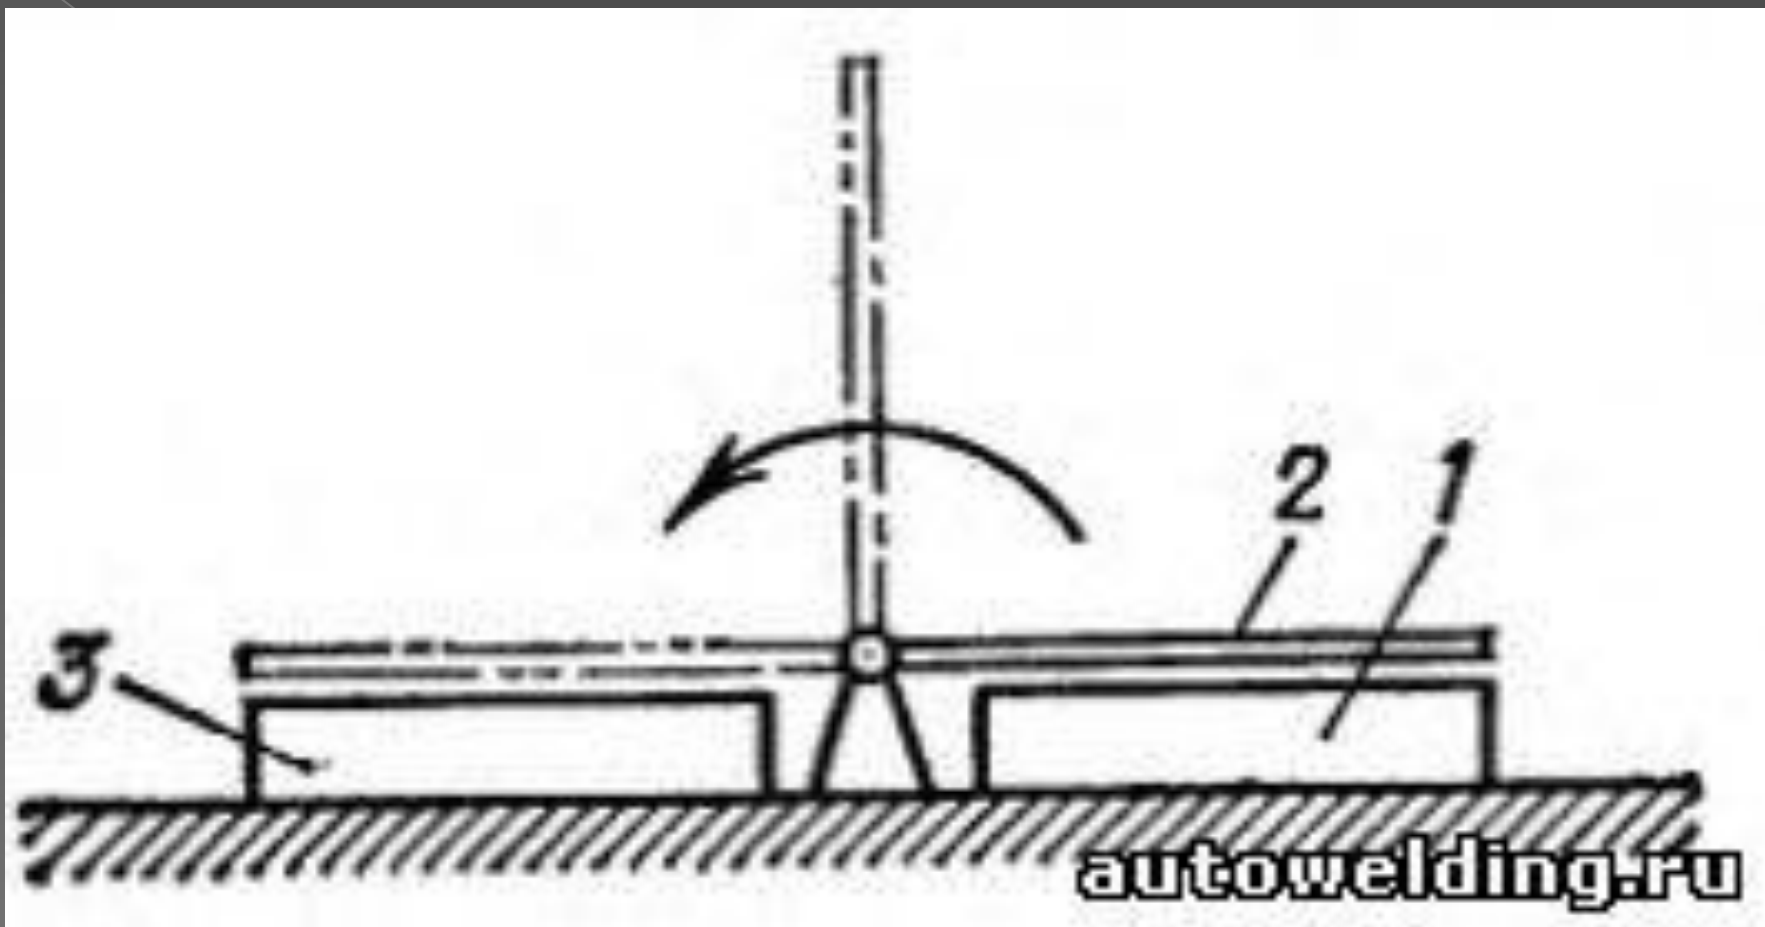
Схема устройства для сборки и сварки ферм: 1-стенд, 2-рамка, 3-стенд.
